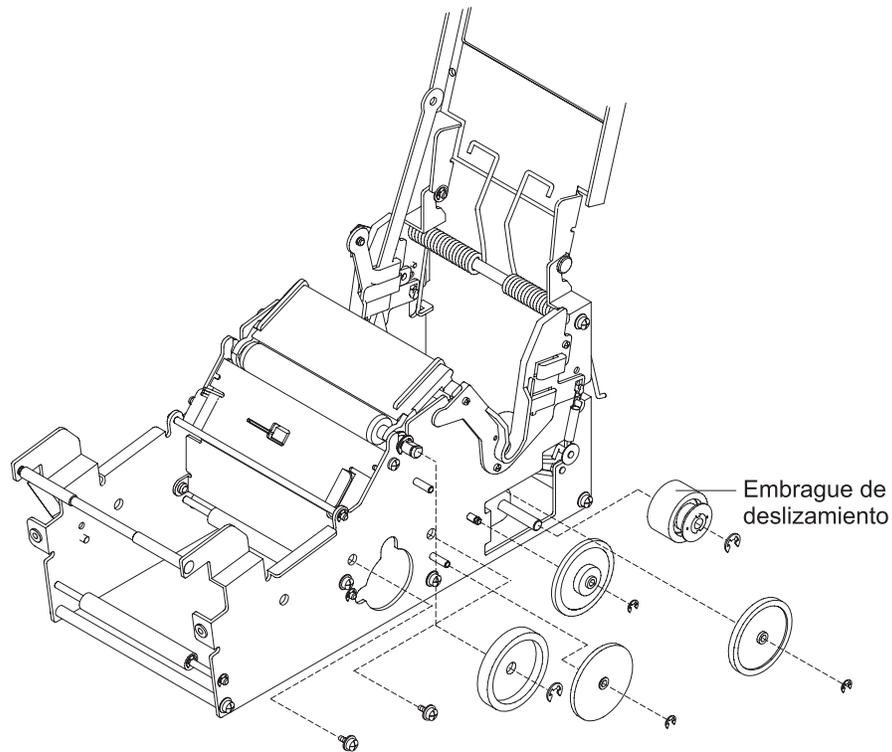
Estación de diario; kit de engranajes con embrague de transmisión y conjunto de pinzas en E
